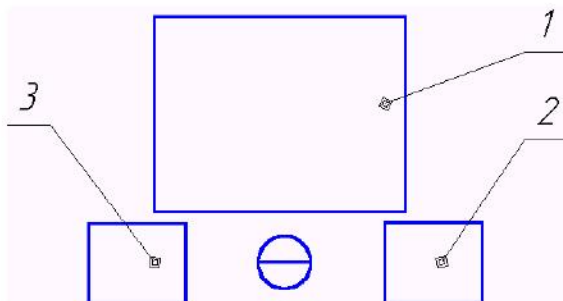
План-схема організації робочого місця штампувальника, що працює від штучної заготовки без застосування засобів автоматизації та механізації: 1 – відкритий кривошипний прес; 2 – ящик для штучних заготовок; 3 – ящик для готових деталей.
